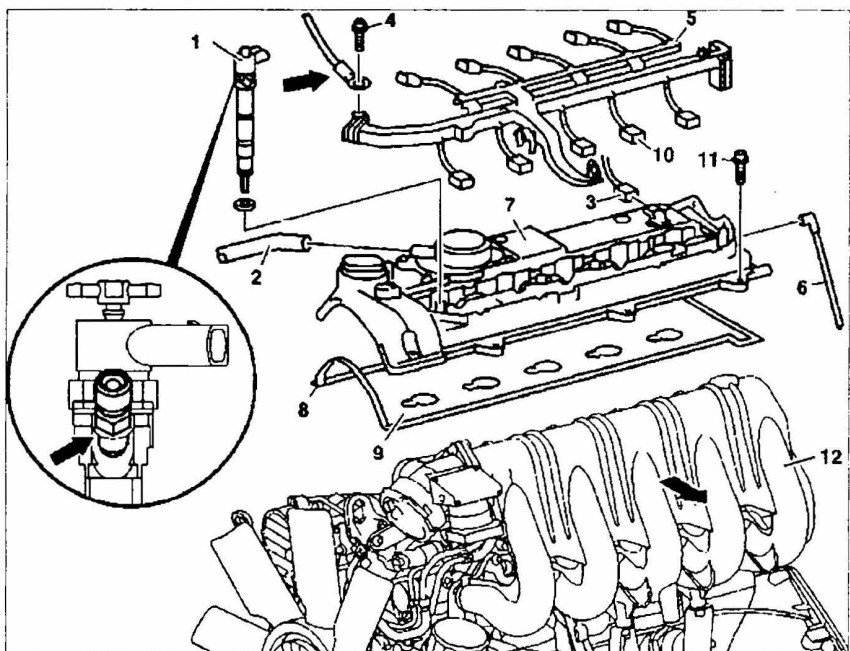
б. Снятие и установка крышки головки блока цилиндров на двигателях 612.981:
